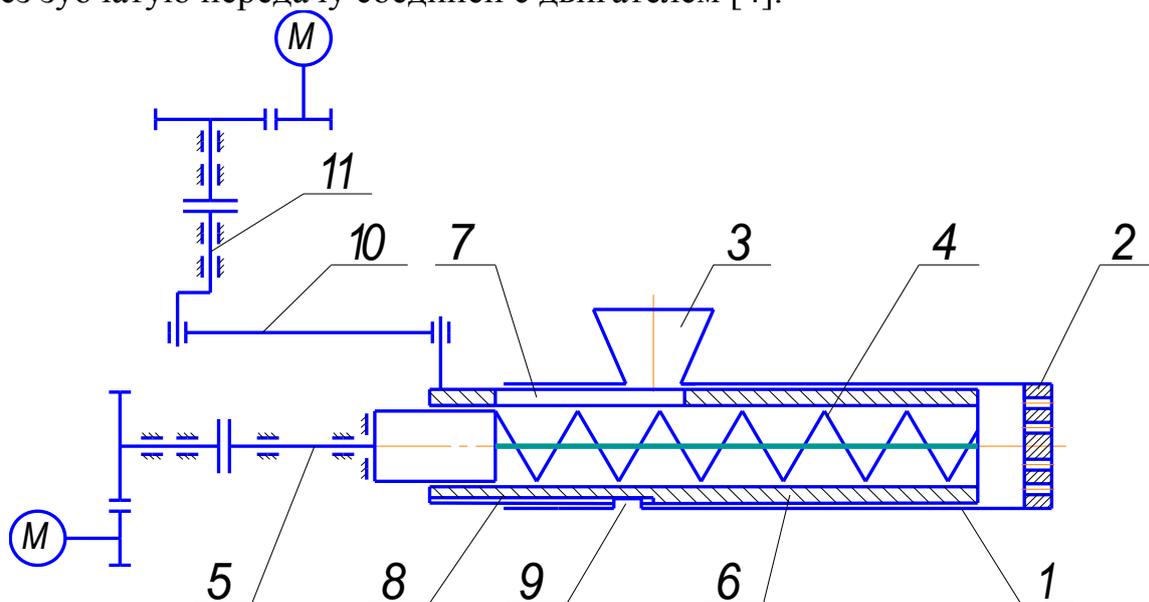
Пресс-экструдер с ползуном кривошипно-ползунного механизма в
